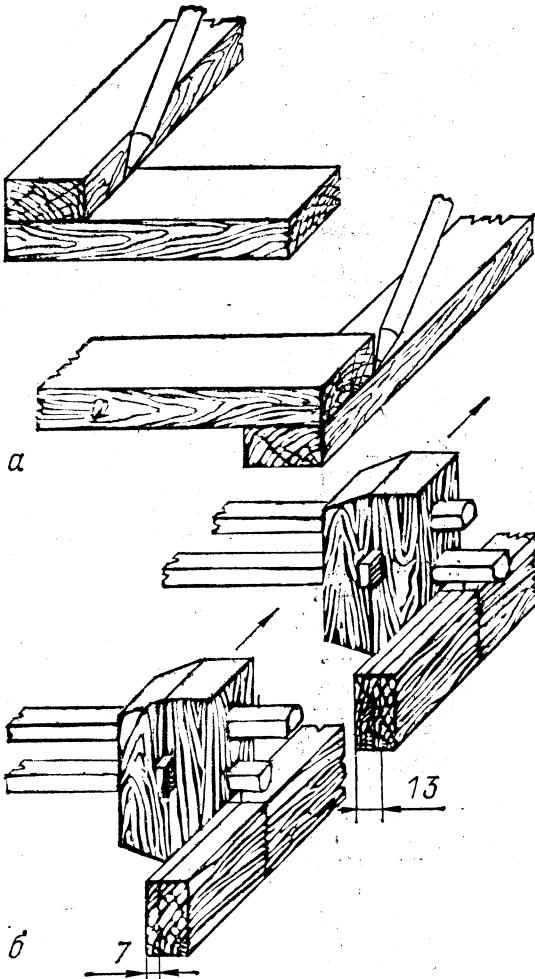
Разметка шипового соединения: а — разметка длины шипа и проушины взаимной накладкой соединяемых брусков; б — разметка толщины шипа и ширины проушины (гнезда) с помощью рейсмуса
